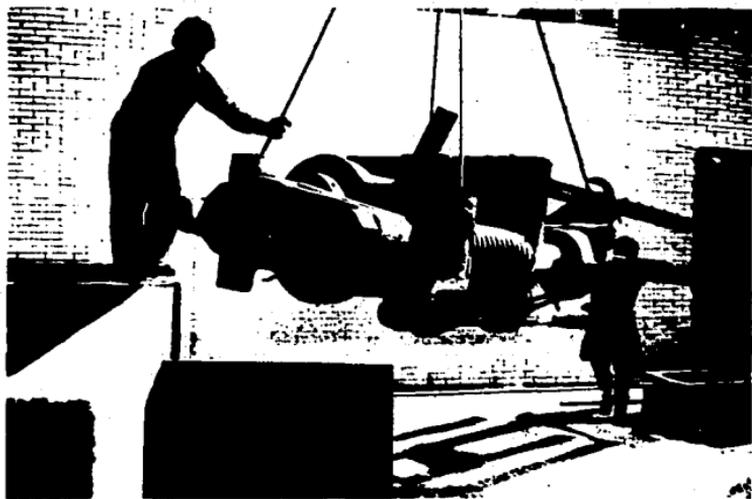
Bajada del marco y tratando de girarlo, para su entrada.
